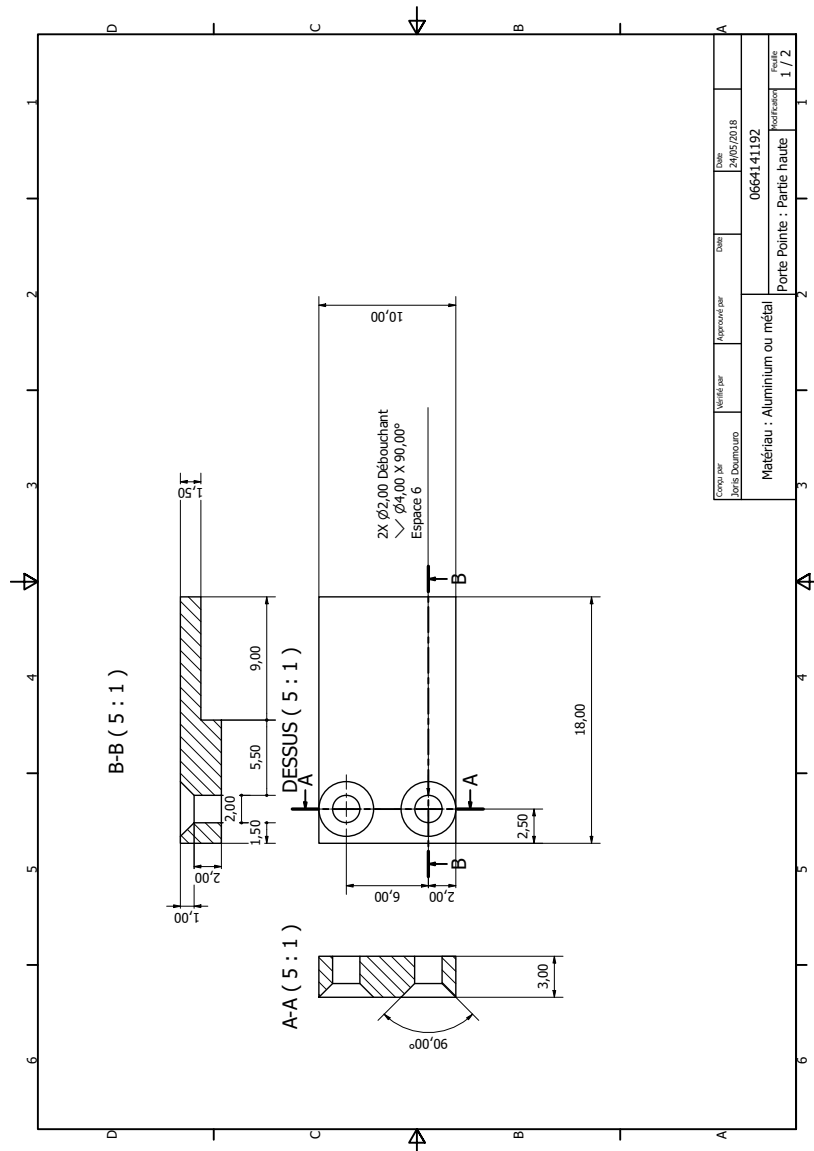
Dessin technique du porte échantillon - partie horizontale : le bec
